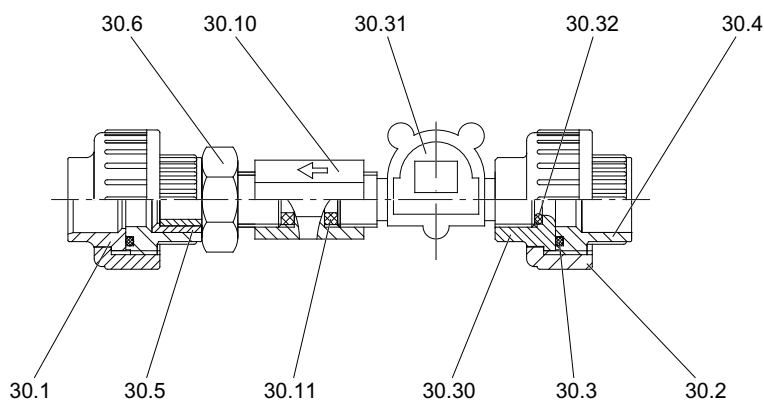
Сборочный чертеж OCD-164-700 до OCD-164-2000
